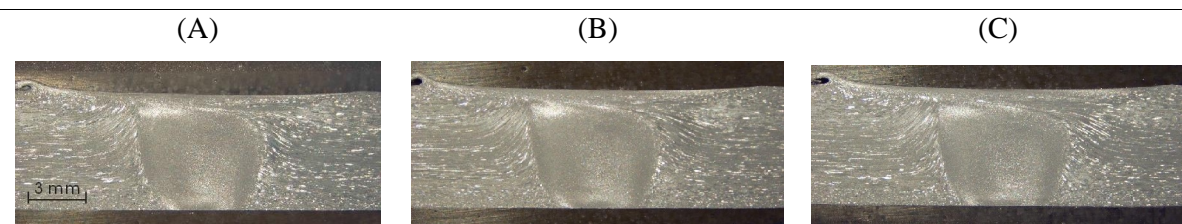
Amostras da seção transversal - ferramenta de soldagem cônica com rosca.
